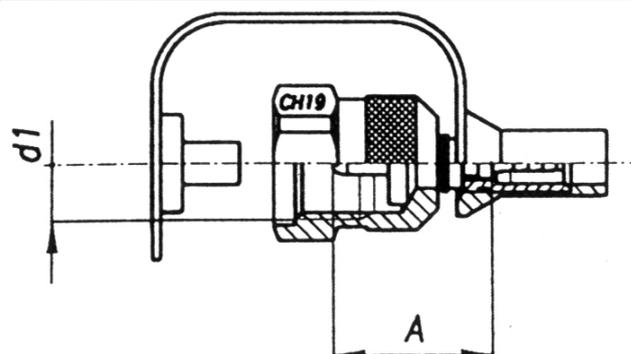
Общий вид фитинга с накидной гайкой и защитным колпачком для присоединения РВДД к гидравлической системе.
